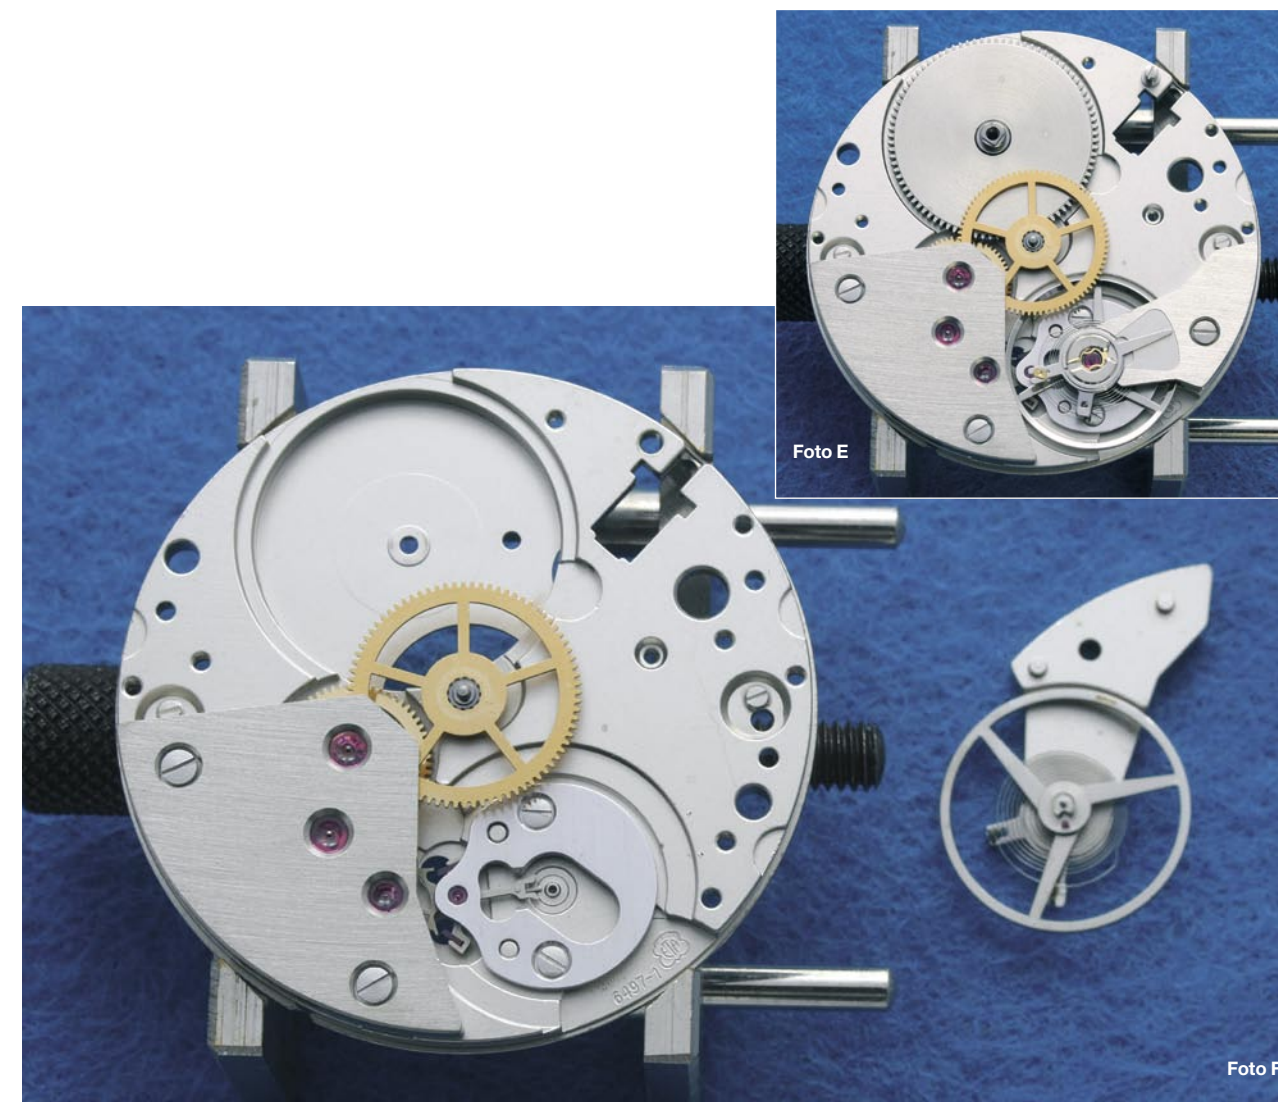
Foto E : Puente del barrilete desmontado. Foto F: Bajo del puente del volante se encuentra el puente del áncora.
